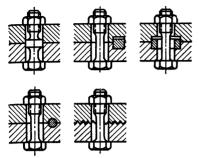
Способы разгрузки резьбового соединения от перерезывающих сил
